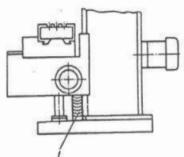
Установка упора под консолью при демонтаже винтовой пары вертикального перемещения стола
